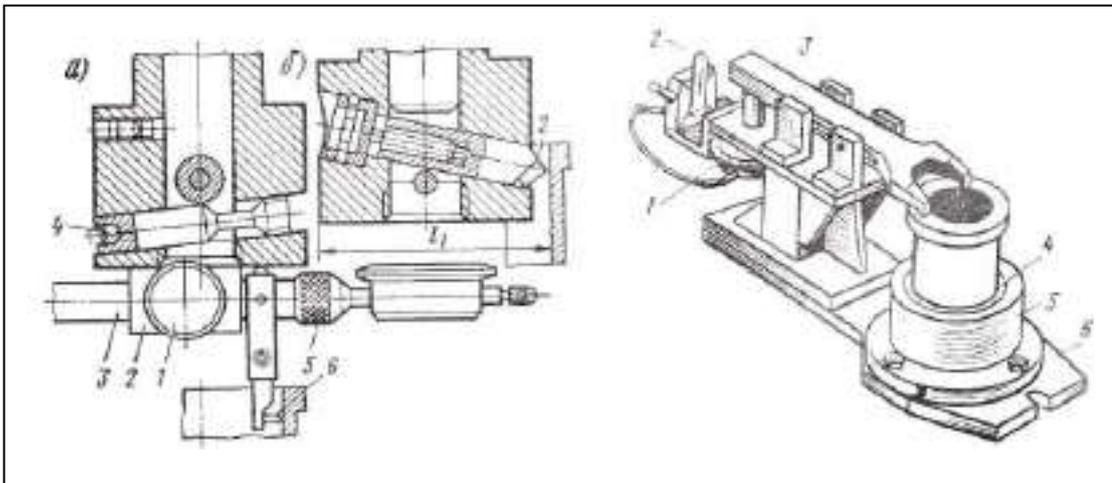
Резцовая головка станка 2А78Н. Рис.21. Приспособление для установки и крепления приспособления для центрирования гильзы (а) и установки резца (б)
